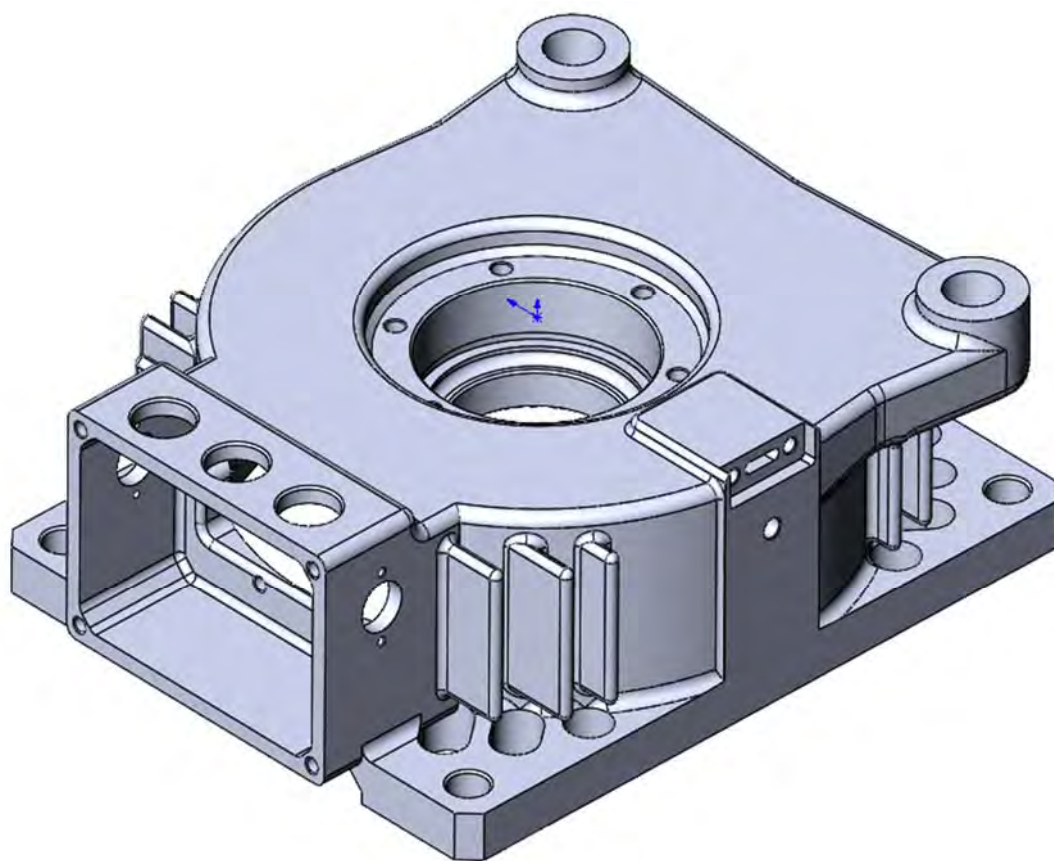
Изометрия щита подшипникового заднего ТАД56
